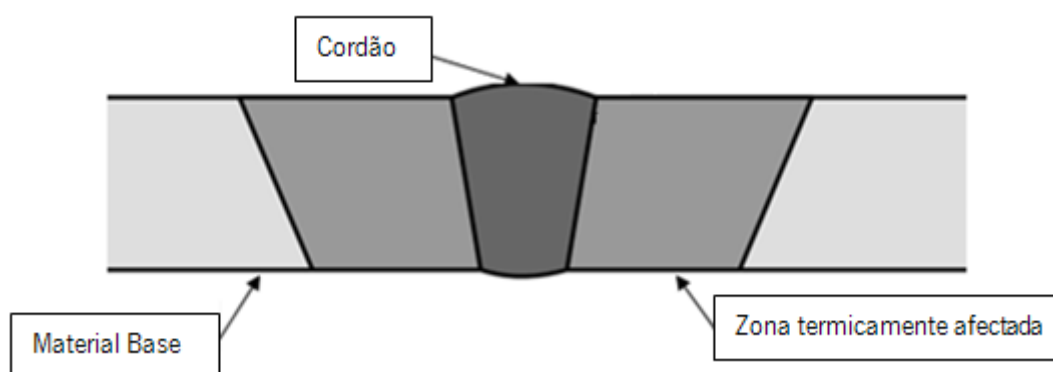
5 - Zonas resultantes da soldadura [5].
